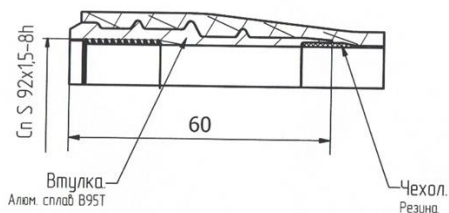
Чертеж соединения с резьбовой алюминиевой втулкой заформованной в стеклопластиковую трубу способом КППН.
